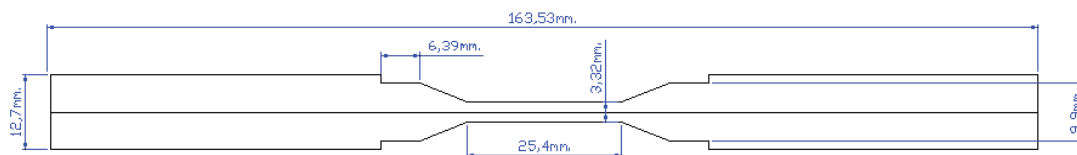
10 Dimensiones de probetas de tensión para placas de 12.7 mm.
